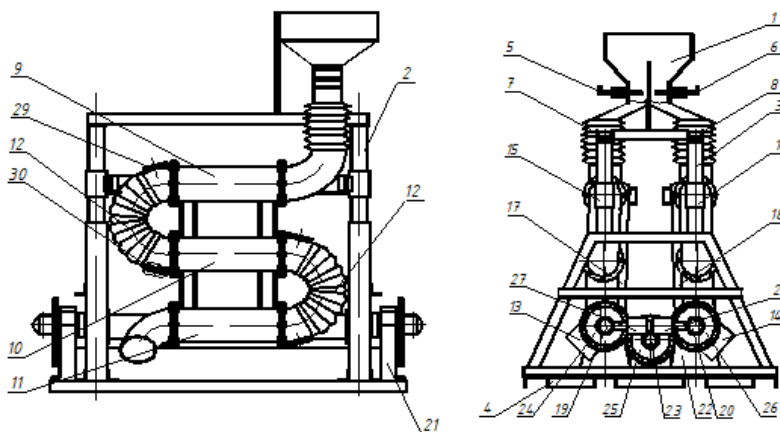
Схема центробежного агрегата с параллельными помольными блоками
